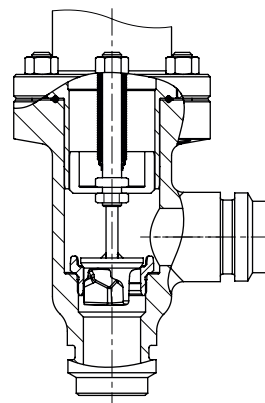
Aluminium-Eckventil Typ 3248, PN 40
